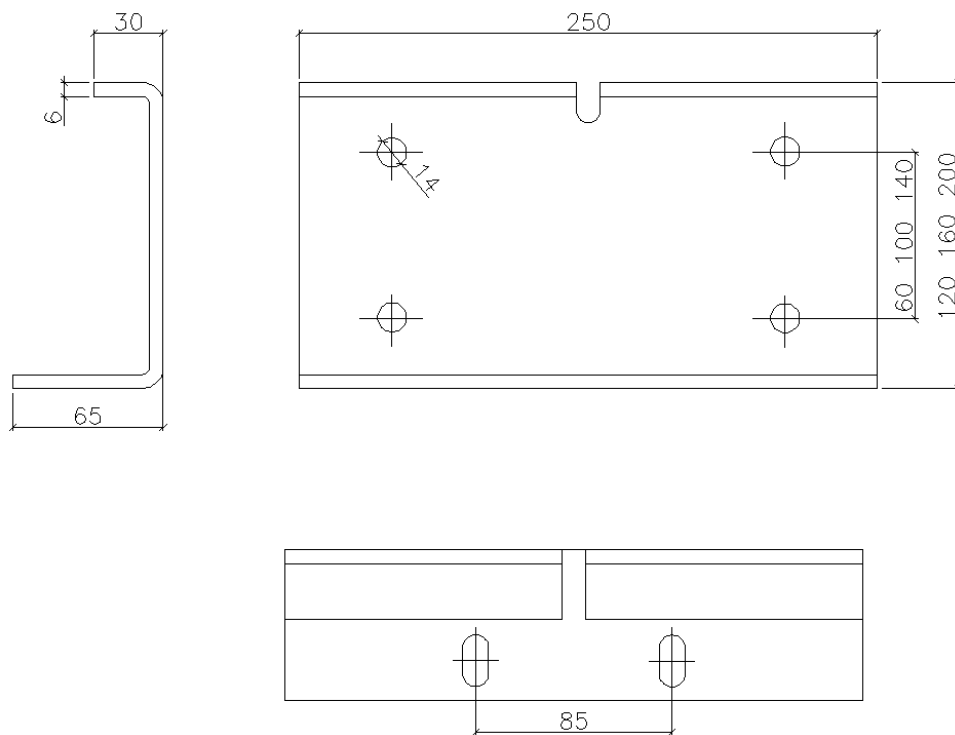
ESQUEMA DE MONTAJE DE VIGA MVH
